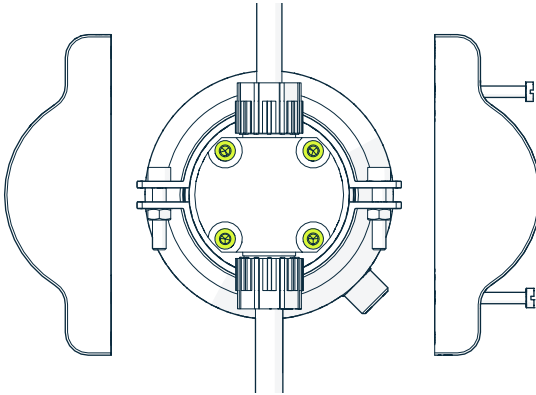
Innensechskantschrauben an den Gewindeschrauben der Endplatte der PR53M Durchflusszelle (integrierte Armaturen)
